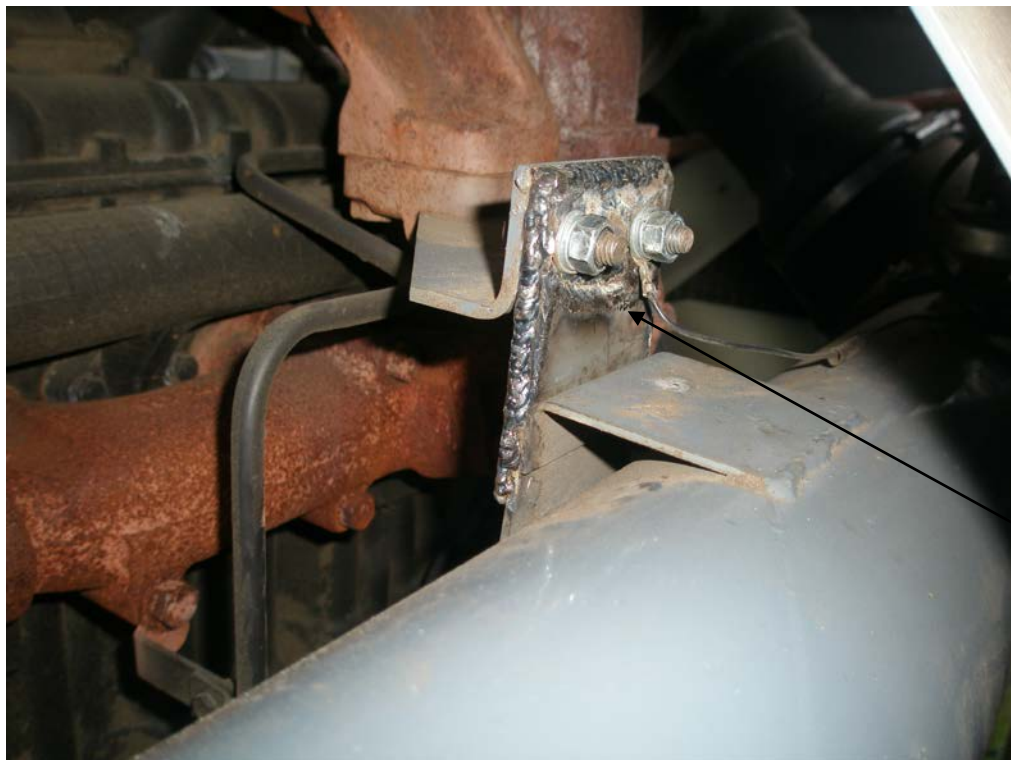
Комбайн зерноуборочный самоходный СК-5 МЭ - «Нива-Эффект» Разрыв пластины крепления воздухопровода, установкой пластины большей толщины
